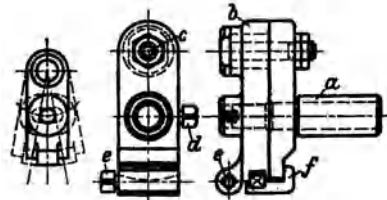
Schwingender werkzeughalter zum Innenausdrehen, dient zum Einstechen und Freidrehen in Bohrungen. Das Kopfstück *b* ist auf dem Schaftteil *a* um Bolzen *c* schwenkbar angeordnet und besitzt eine Aufnahmebohrung zum Einspannen des Werkzeuges durch Schraube *d*. Die Planbewegung erfolgt über die Druckschraube *e* vom Querschlitten aus. Eine Gegenführung *f* verhindert ein Flattern des Kopfstückes beim Einstechen.
